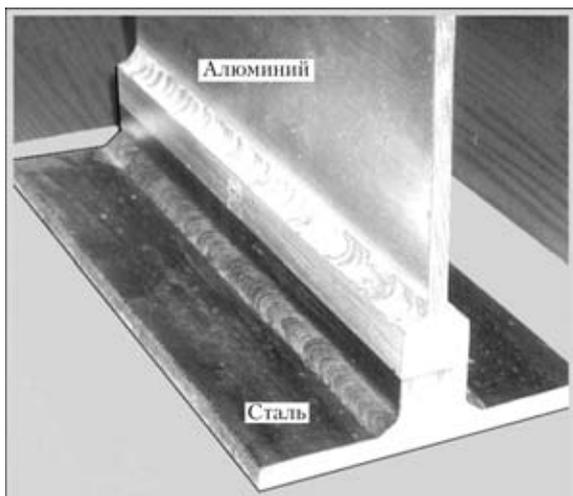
Соединение алюминия со сталью, выполненное дуговой сваркой через биметаллический переходник, полученный СВ
